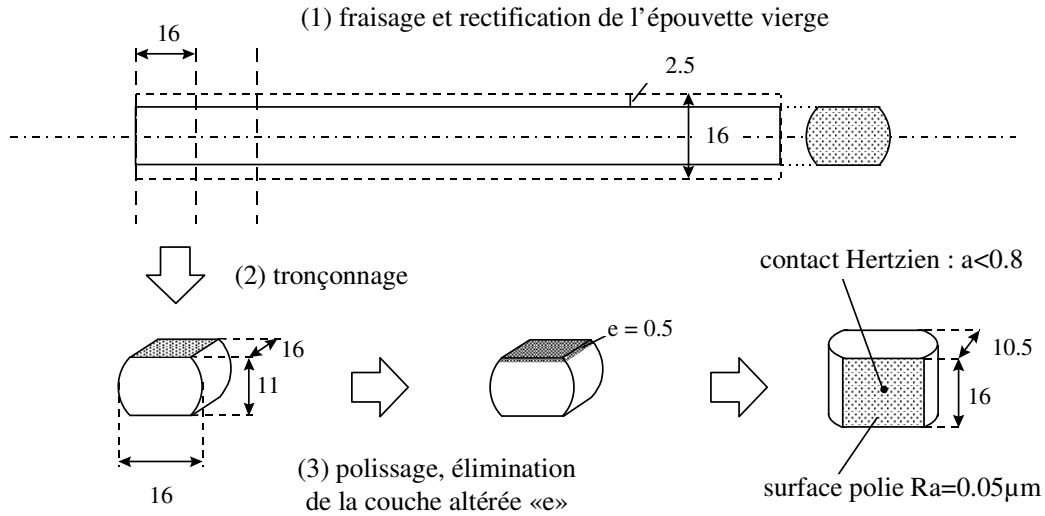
Illustration de la préparation des échantillons de fretting à partir des éprouvettes vierges de 30NCD16 (dimensions en mm).
